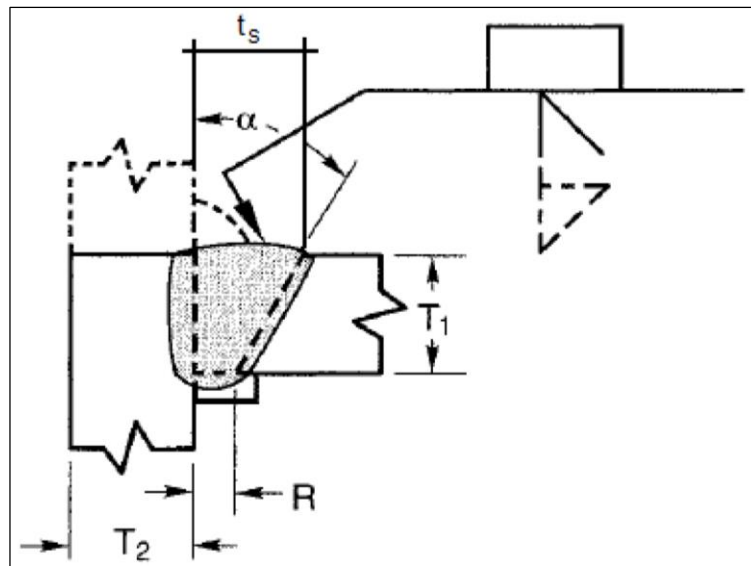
Geometría de soldadura de penetración completa
